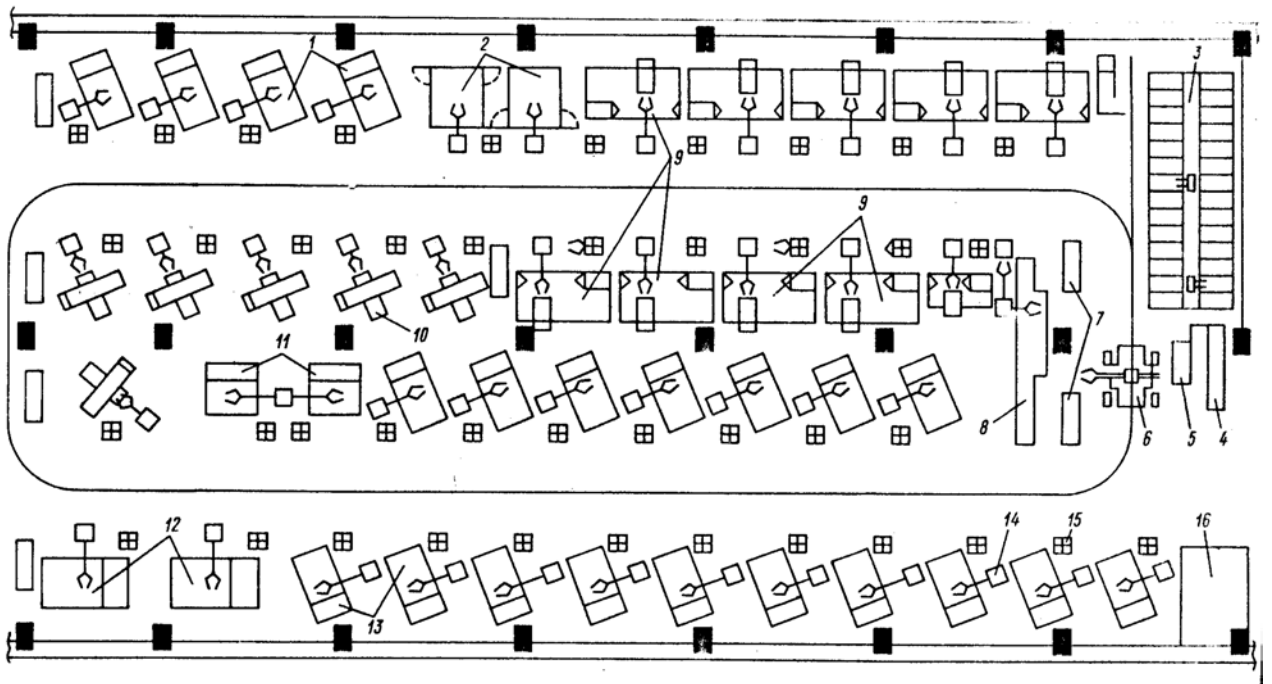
Роботизированный цех механообработки: 1, 2, 11, 12, 3 — токарные станки; 3 — склад; 4 — загрузочное устройство; 5 — разгрузочное устройство; 6 — напольные транспортные ПР; 7 — промежуточные склады; 8 — протяжной станок; 9 — шлифовальные станки; 10 — фрезерные станки; 14 — ПР; 15 — магазины; 16 — пульт диспетчера
